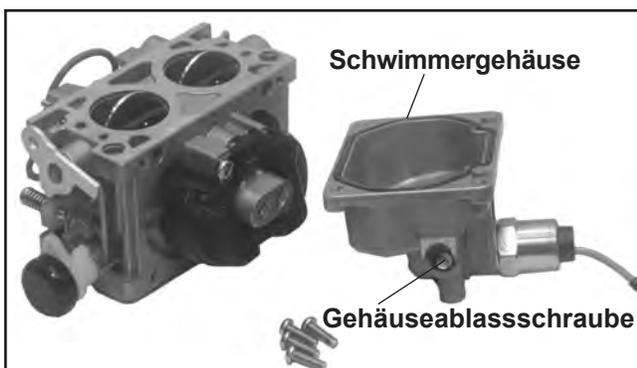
Schwimmergehäuse ohne Kraftstoff.
